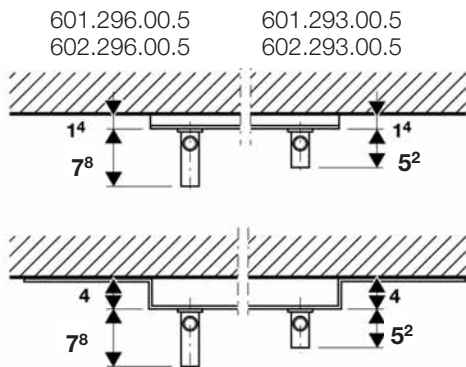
Profundidad de instalación en aplique con placa de montaje 601.731.00.1 a 601.738.00.1
